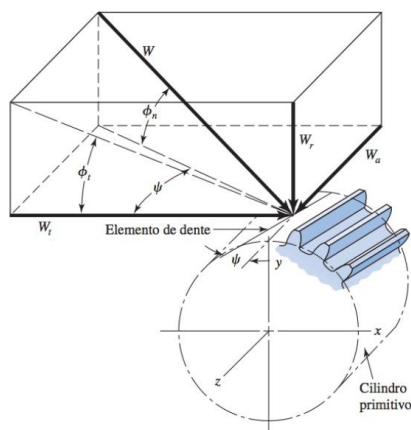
Esquema de decomposição de forças engrenagem helicoidal
